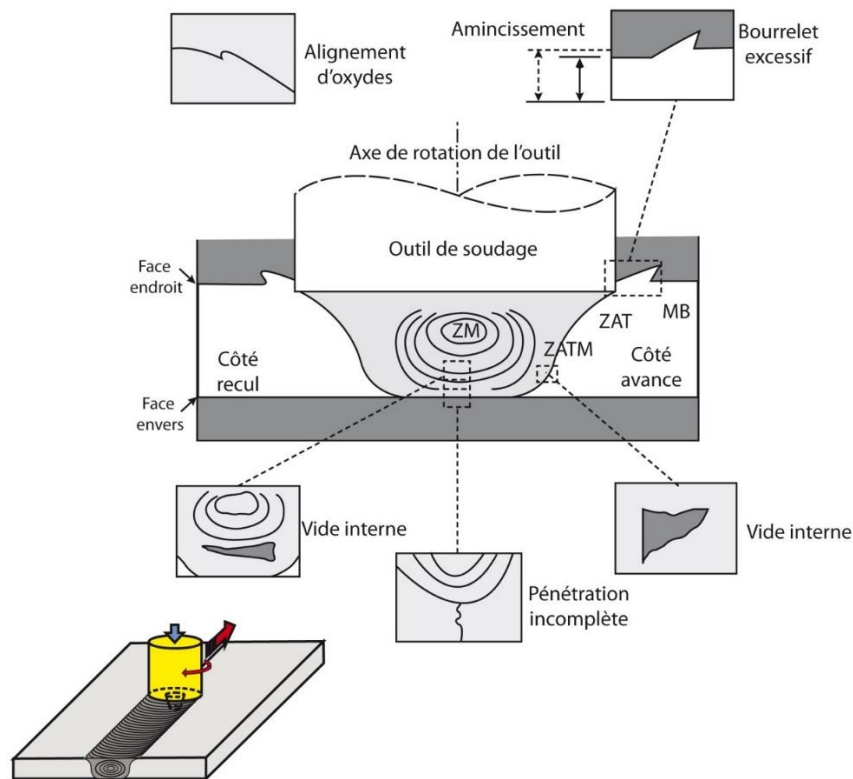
Schéma montrant la position des défauts en soudage FSW en soudure bout à bout.
